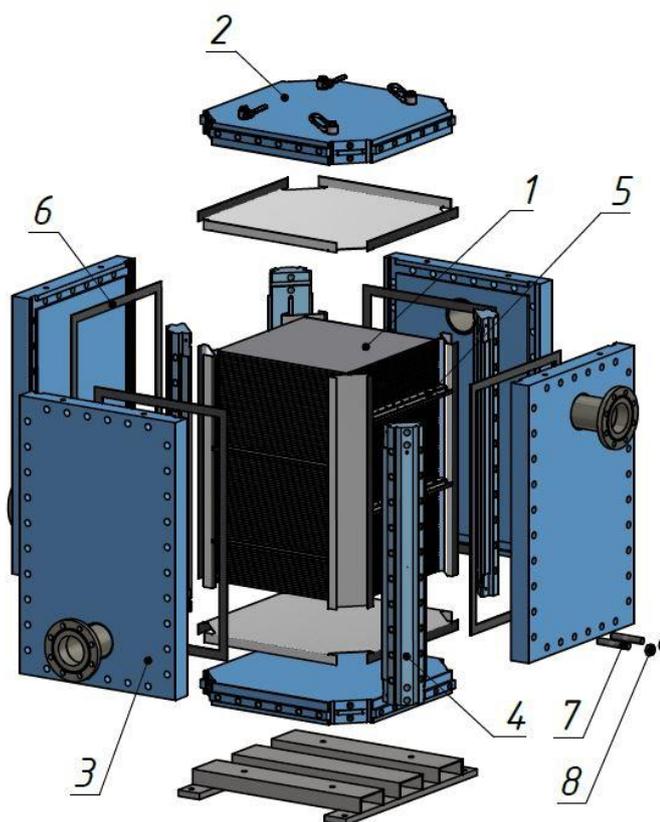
Аппарат теплообменный пластинчатый сварной типа SB
